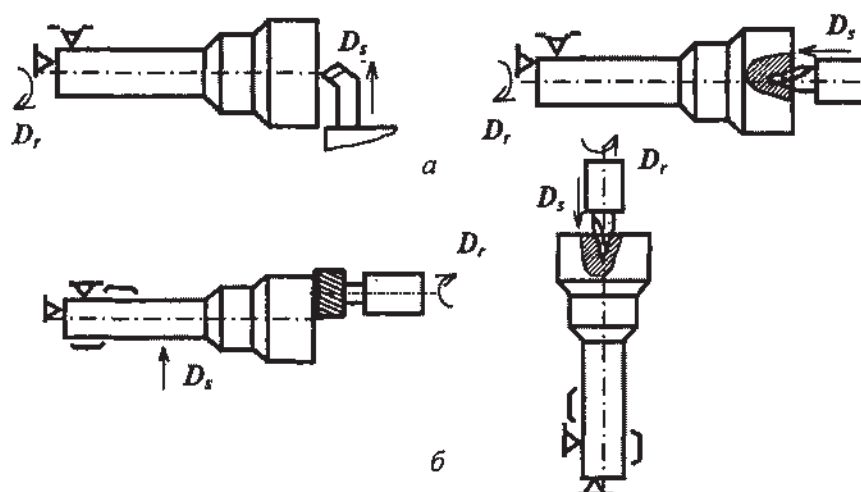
Схема обработки торцов и центровых отверстий на универсальном токарном станке (*a*) и горизонтально-фрезерном и сверлильном станках (*б*)
